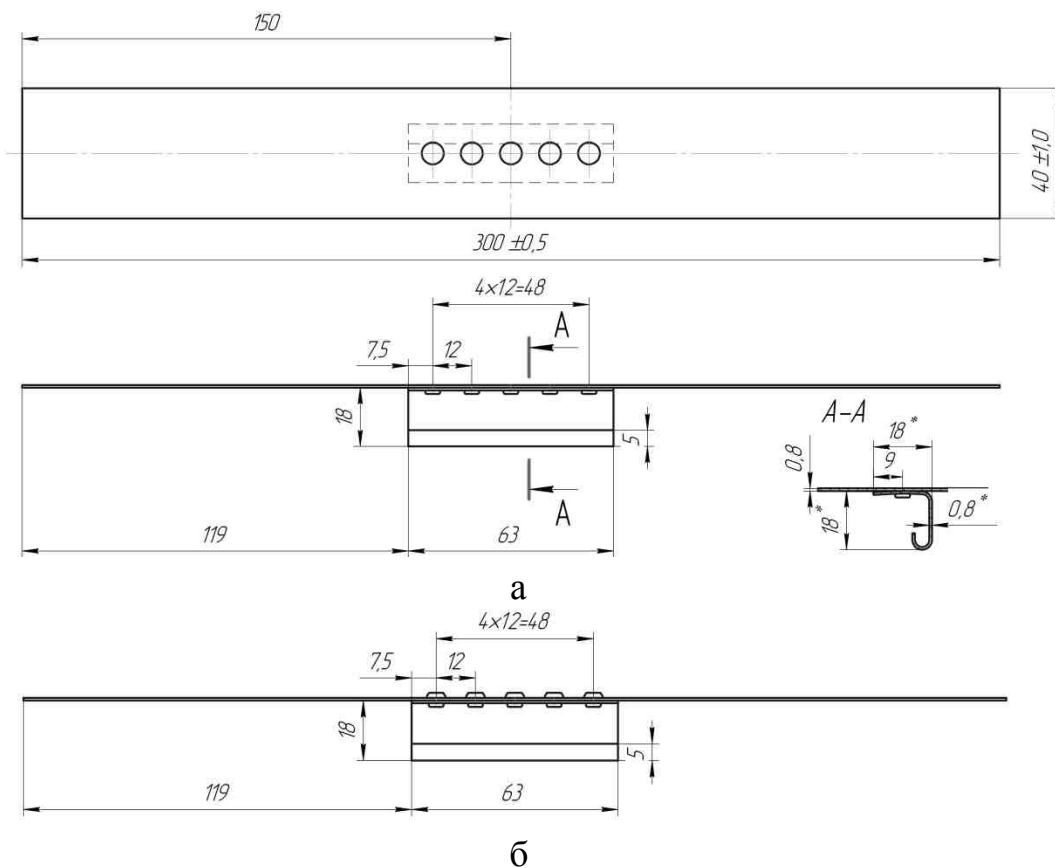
Фрагмент чертежа соединения с одной накладкой и шагом заклепок 12 мм: а – с потайными заклепками; б – с заклепками с плоско-скругленной головкой
